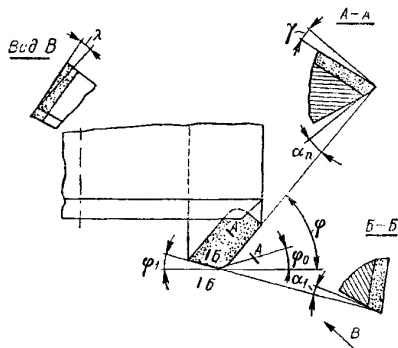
Основные углы режущей части зуба фрезы
